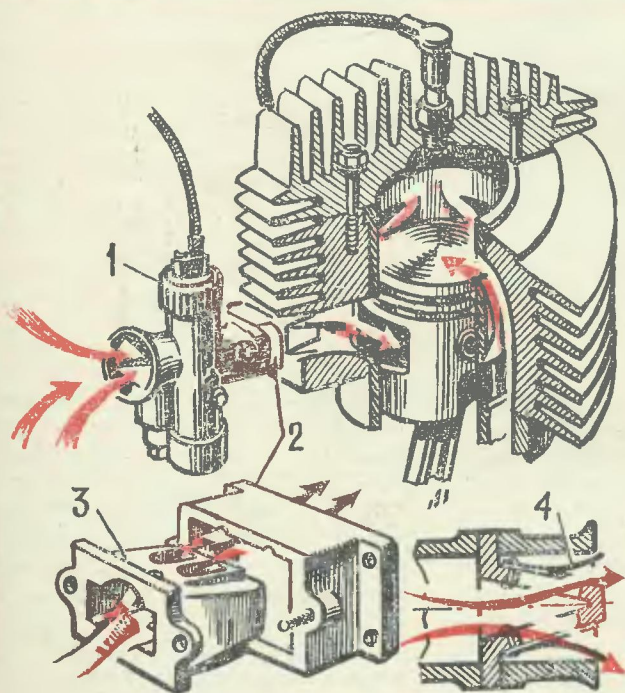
Устройство и работа лепесткового золотника (клапана) в двигателе японской фирмы «Ямаха»: 1 — карбюратор, 2 — промежуточный патрубков, 3 — корпус клапанов, 4 — лепестковый клапан.
